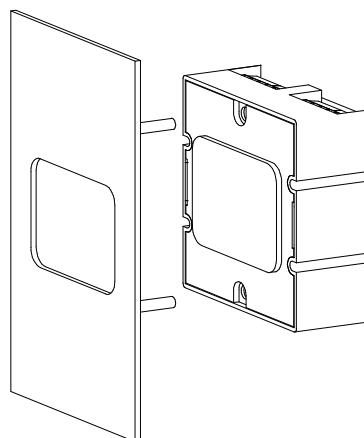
Display para fijación con pernos soldados en botonera
